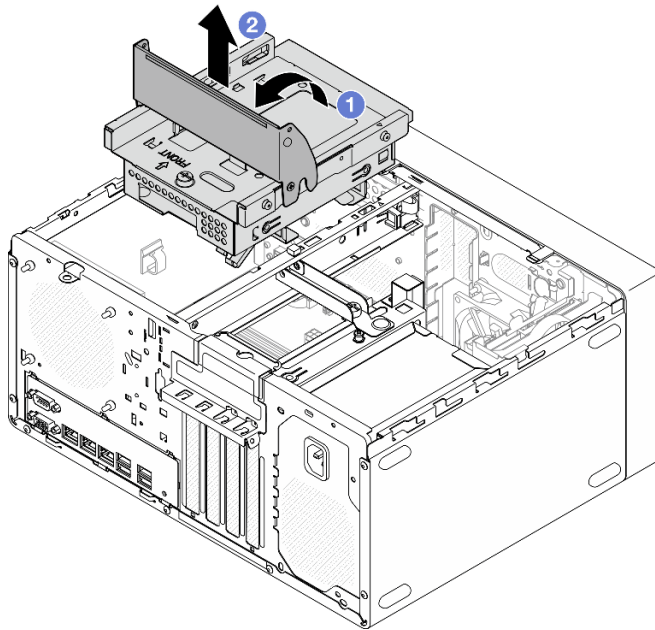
Entfernen der Halterung für das optische Laufwerk
